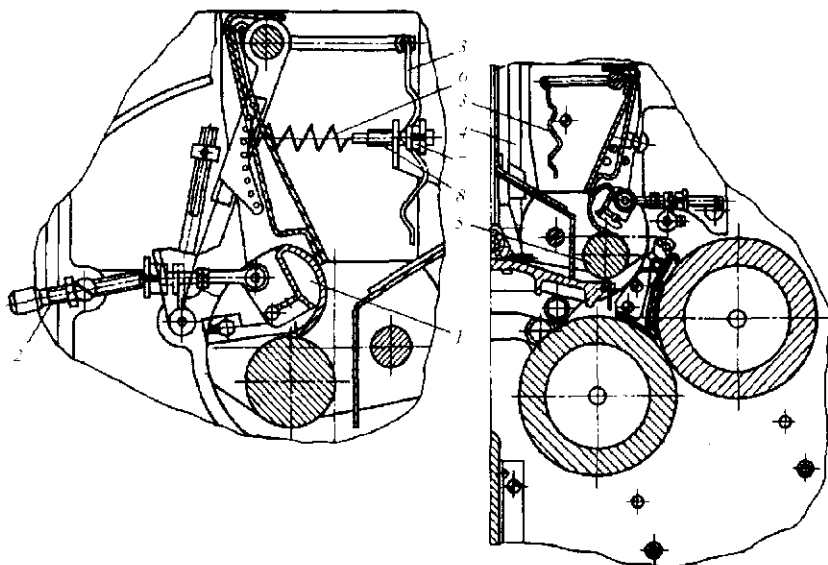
Устройство автоматического регулирования подачи зерна
